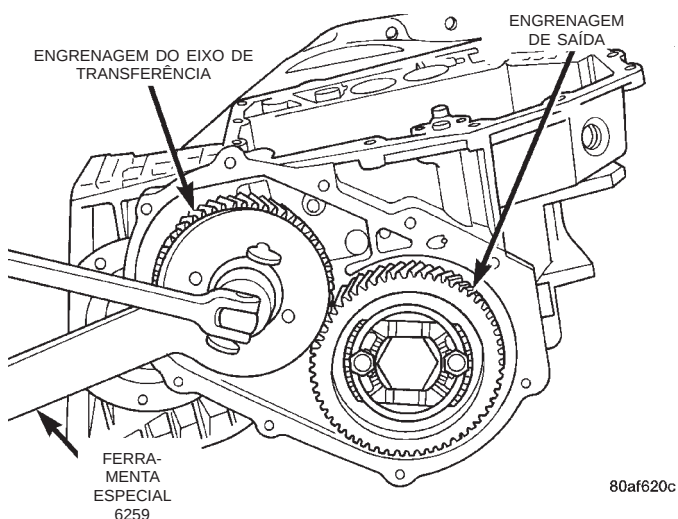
Remoção da Porca da Engrenagem do Eixo de Transferência
